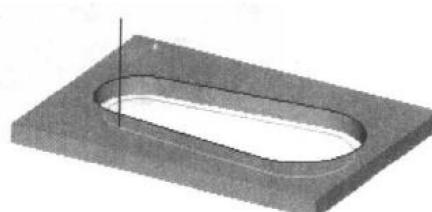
平面轮廓加工实现轮廓腔零件的精加工
